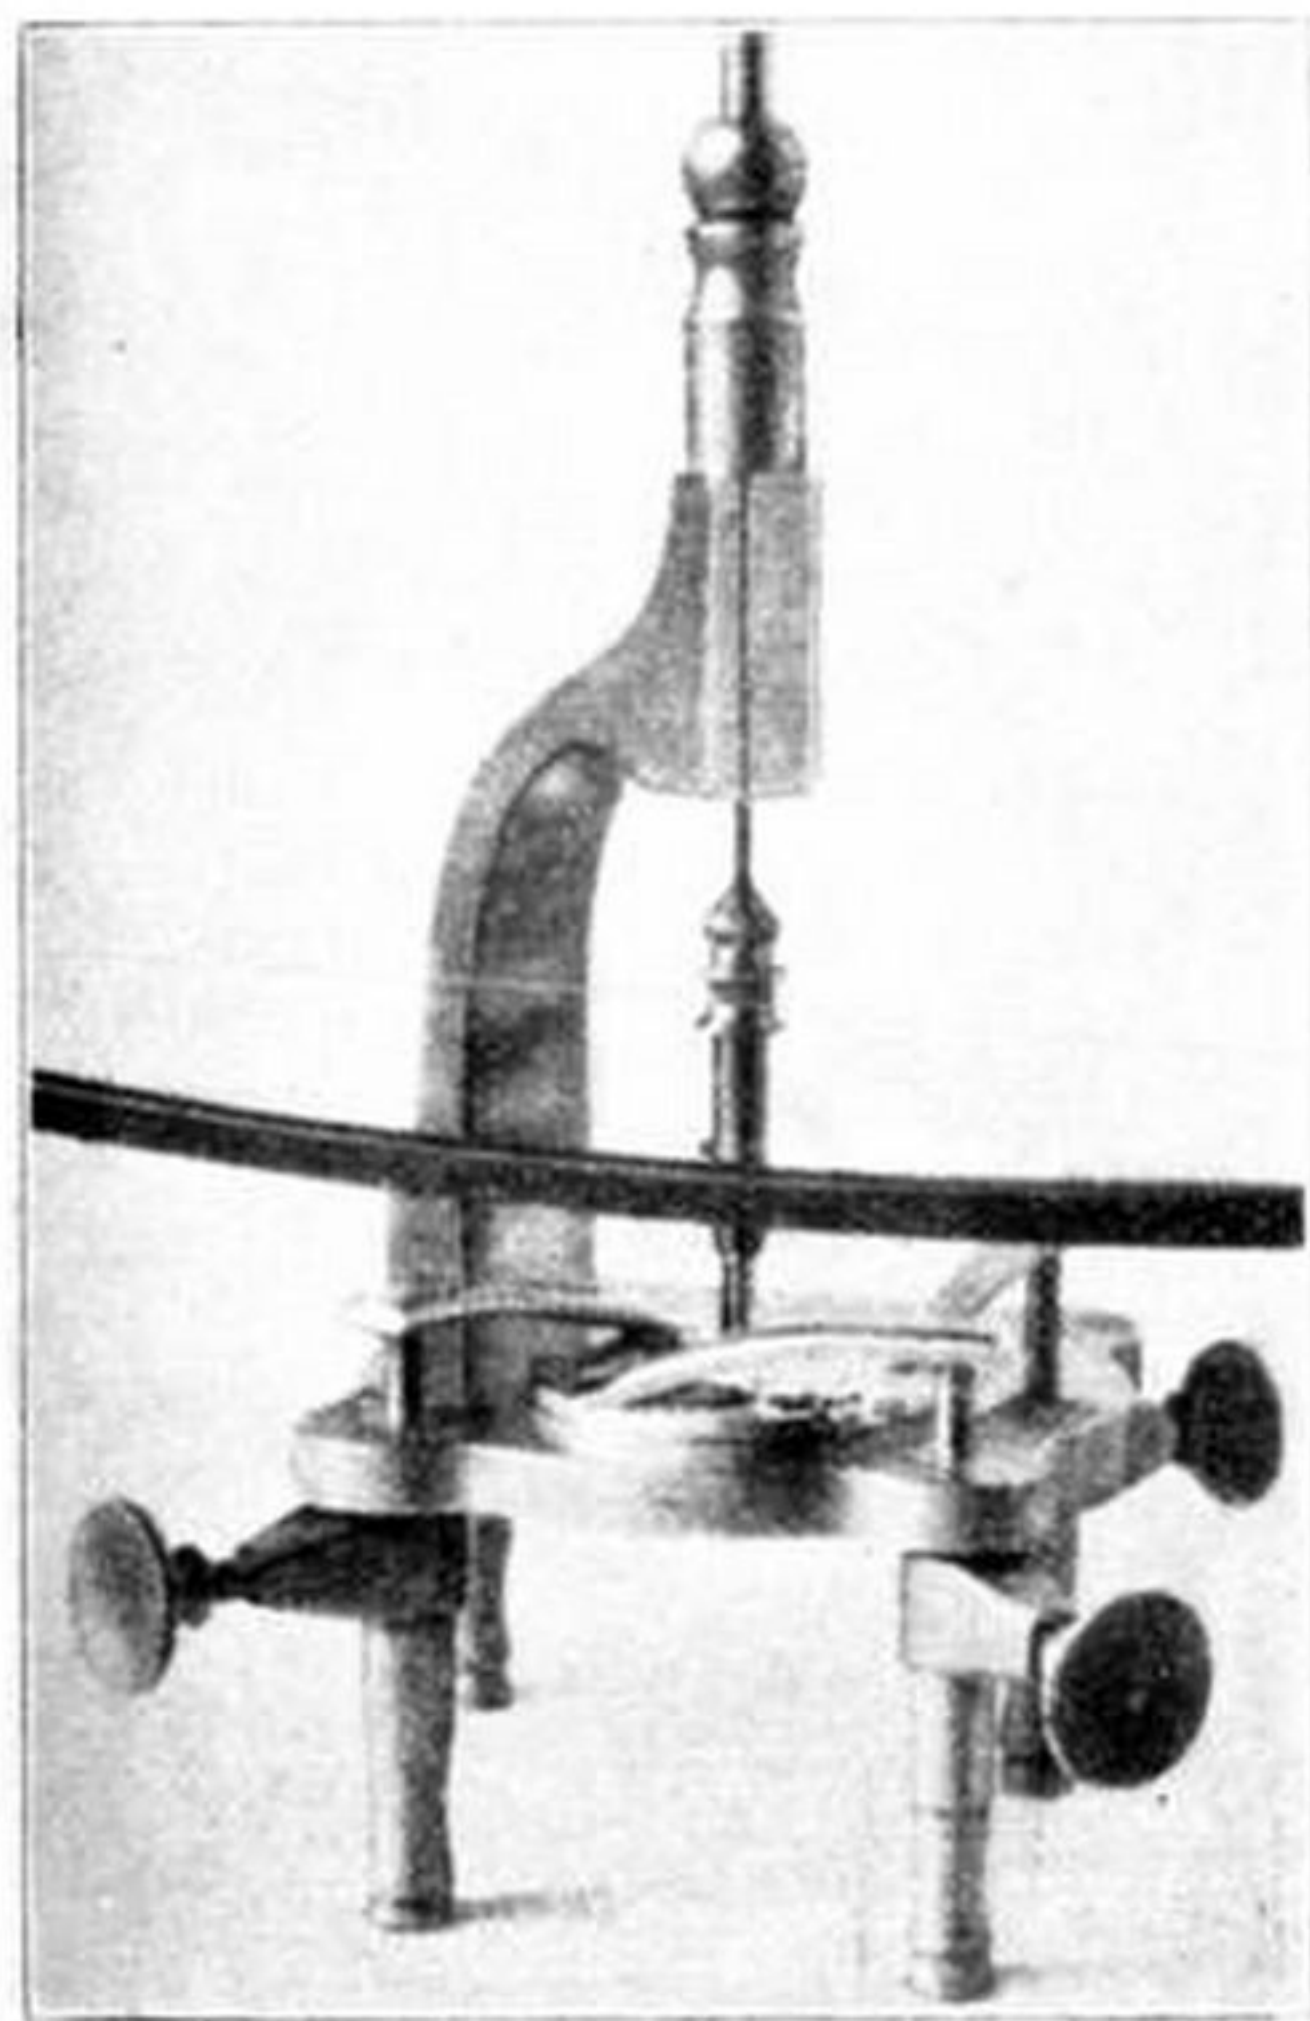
Fräsen einer Fassung in der Geradebohrmaschine
